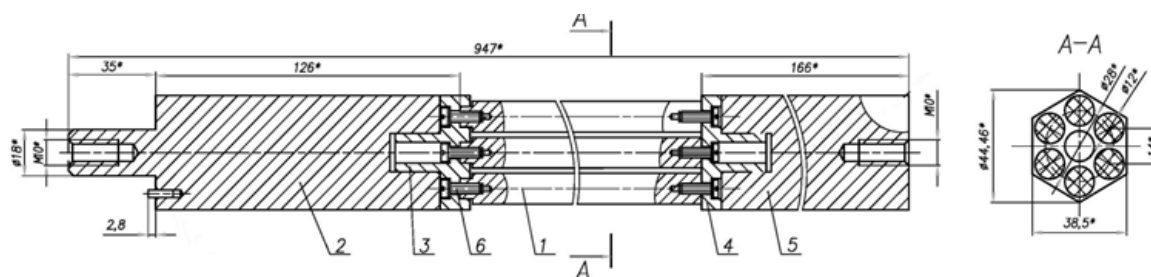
Топливная кассета критической сборки: 1 — твэл; 2 — хвостовик; 3 — нижняя трубная пластина; 4 — верхняя трубная пластина; 5 — головка; 6 — винт.
